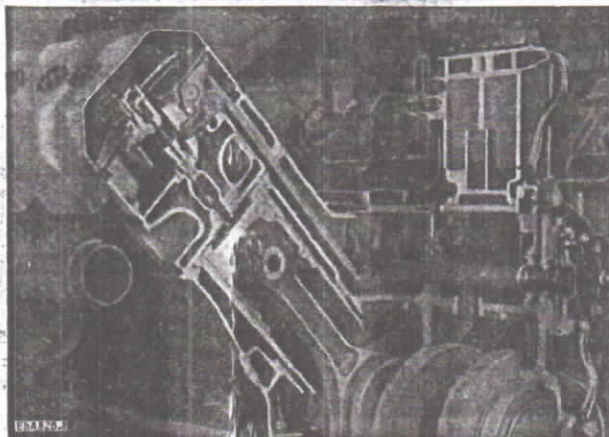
Dieselmotor 8 KVD 21 T, Zylinder- und Gehäuseschnitt
